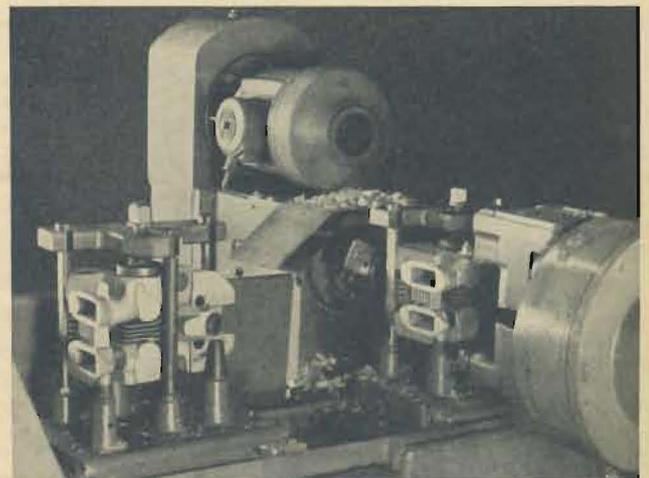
Maschine mit Bohrkopf für die Bearbeitung des Kompressionsraumes und vierspindeligen Fräskopf für das Fräsen der Schraubenauflagen
